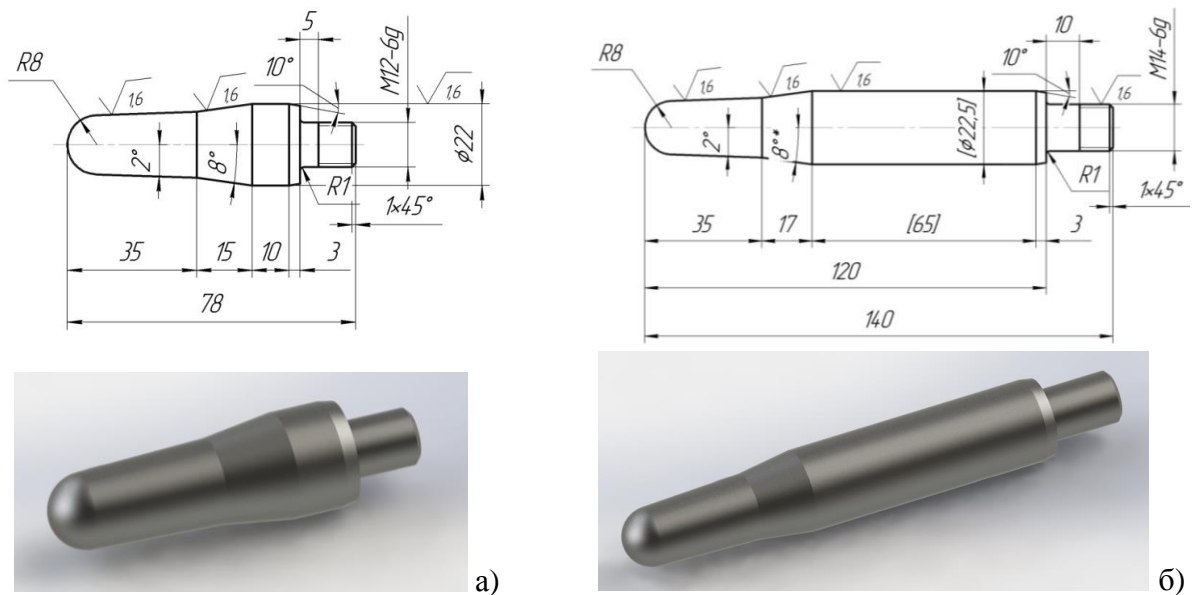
Оправки прошивного стана «30-80» для прошивки заготовки диаметром 35 мм:
